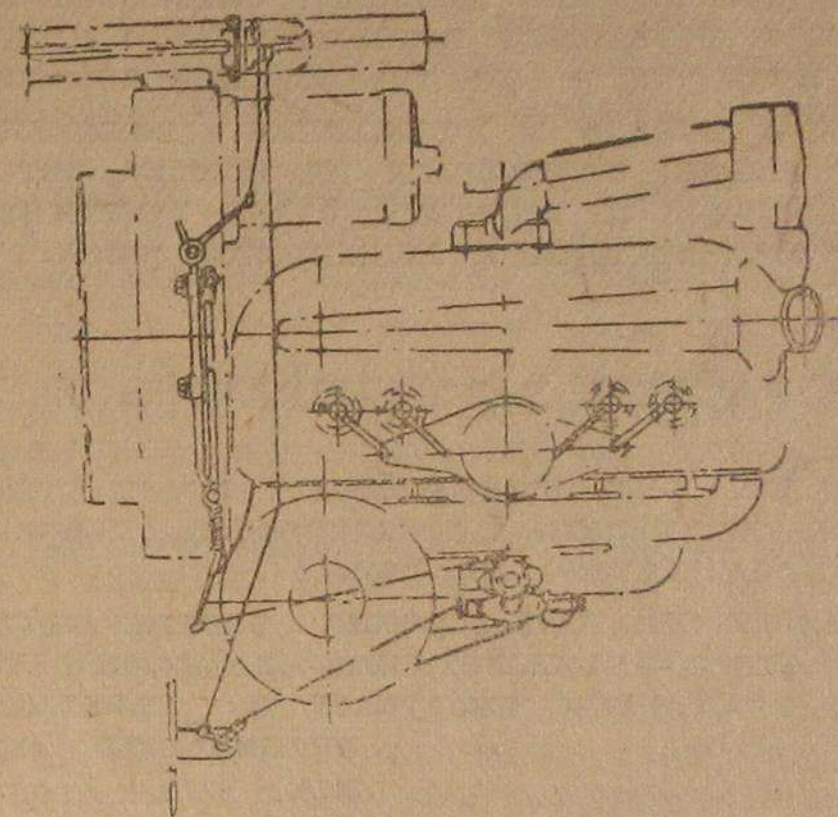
Управление смесителем и карбюратором двигателя (вид сверху).
